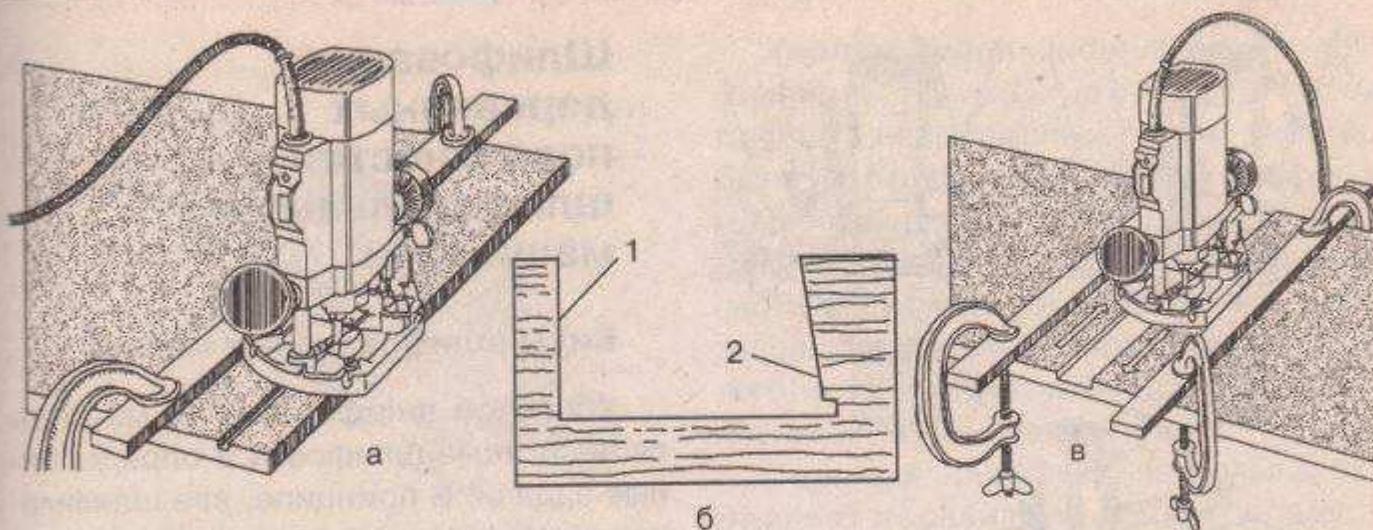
Вырезание пазов для врубки: а — узкого на широкой доске; б — одностороннего «ласточкина хвоста»; в — широкого паза; 1 — фрезерование прямой фрезой; 2 — фрезерование фрезой «ласточкин хвост»
